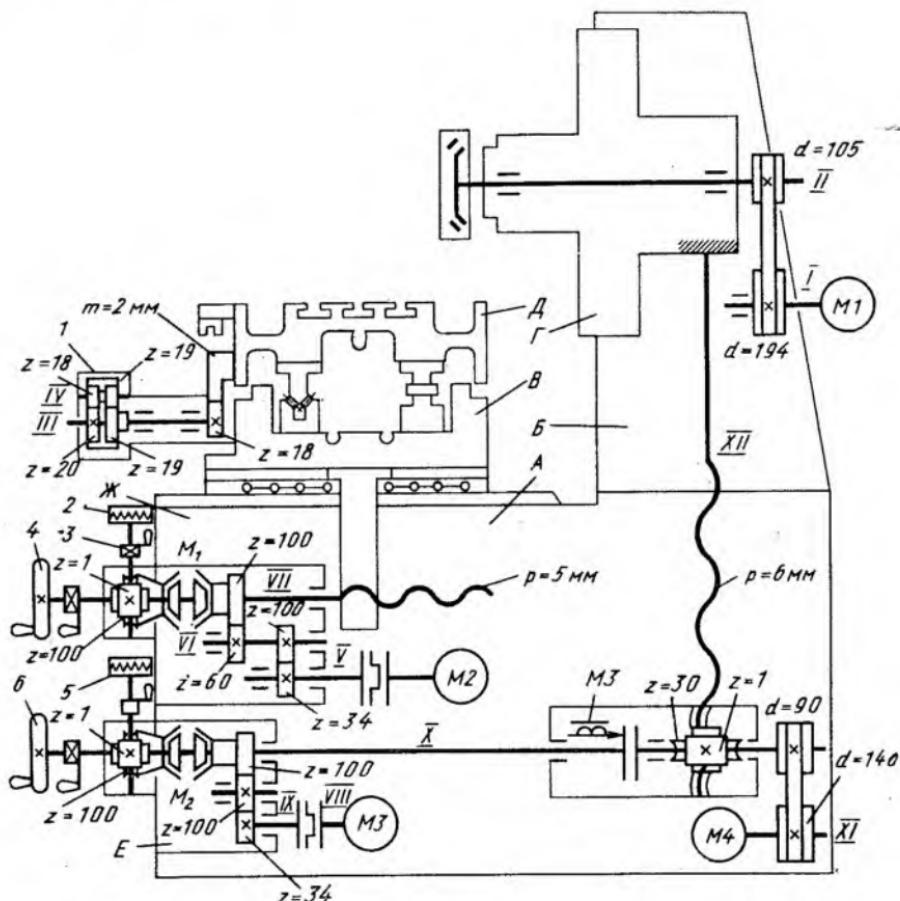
Кинематическая схема плоскошлифовального станка ЗЕ711Б:
